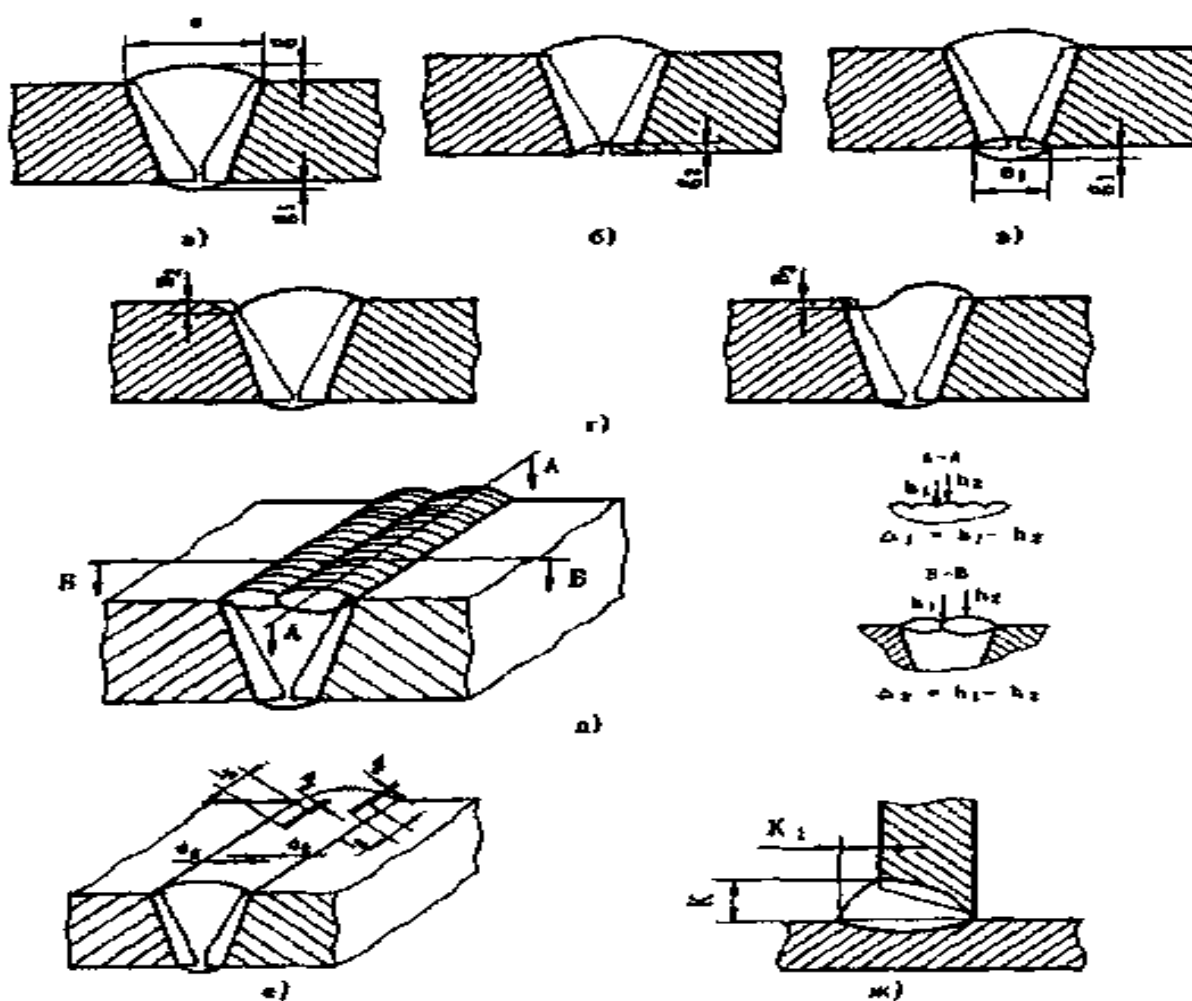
Конструктивные элементы сварных соединений:
